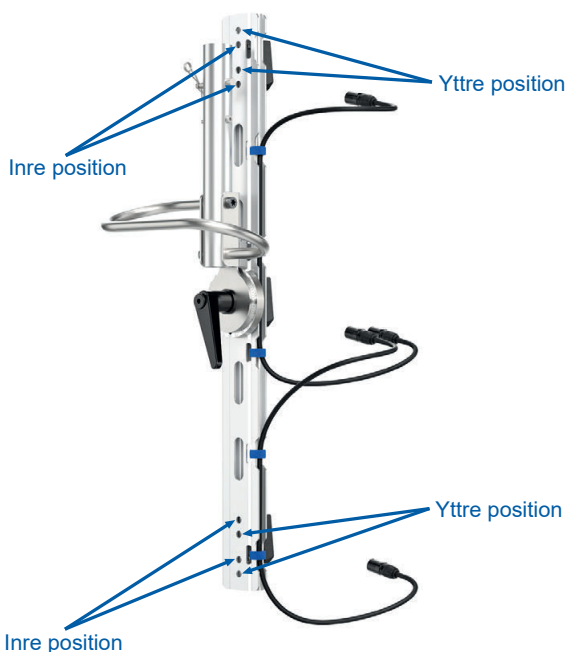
Justering av Quick Lock Mounts (snabblåsfästena)
